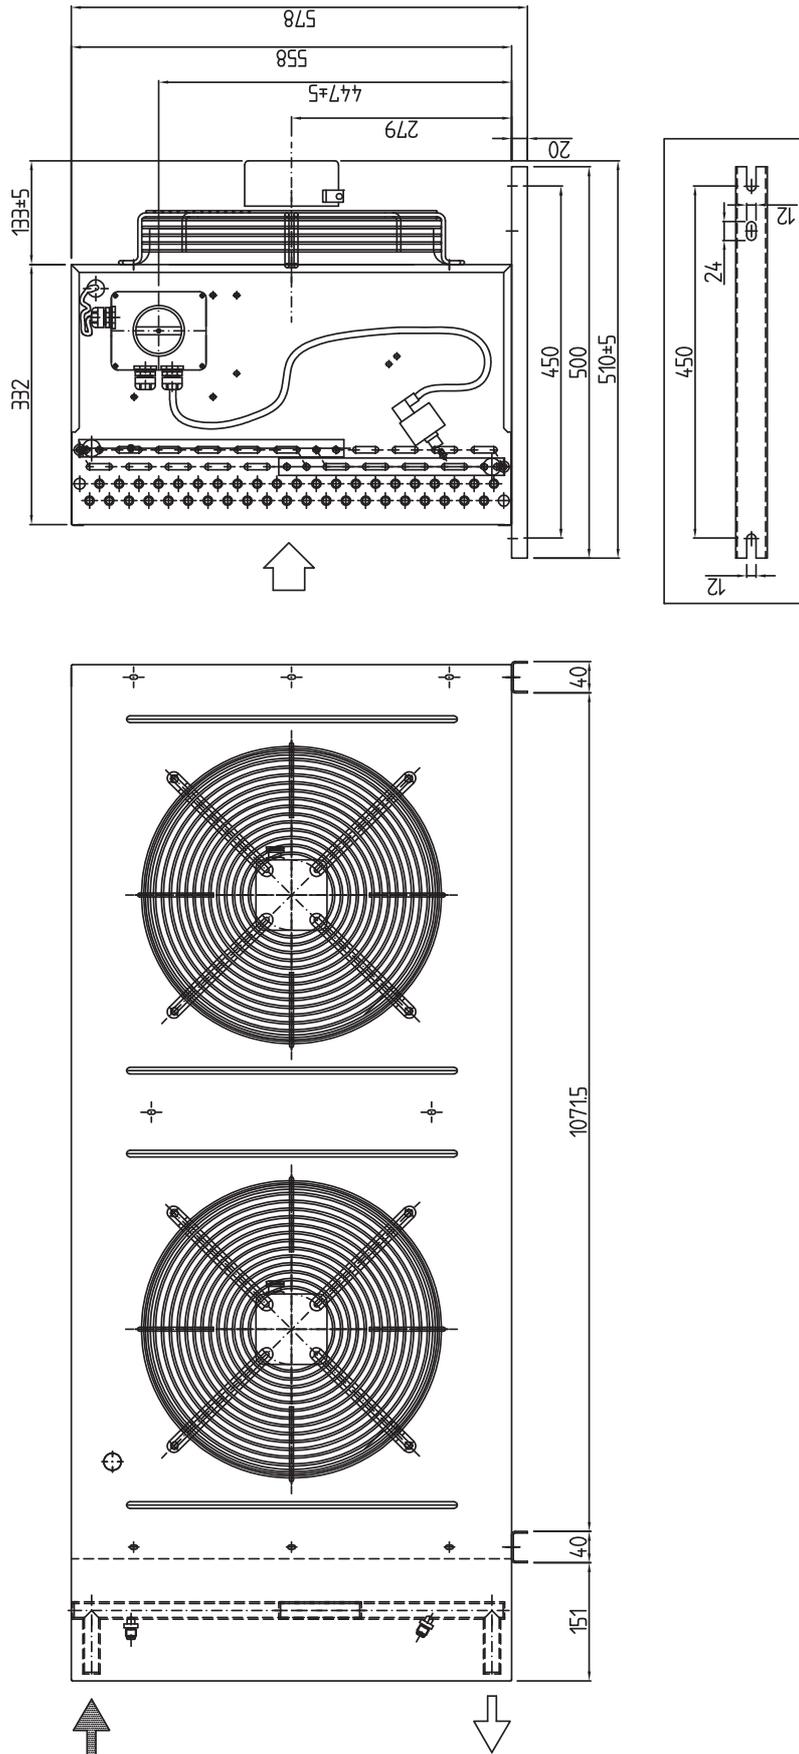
Condensador estándar 3311.360 (montaje a fachada)
